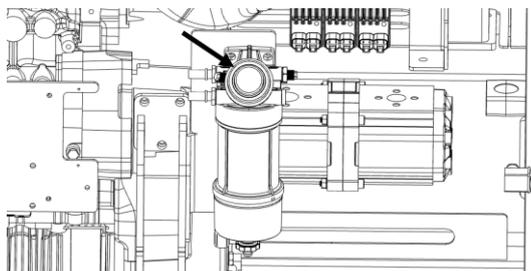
Posizione del filtro del carburante con separatore d'acqua
